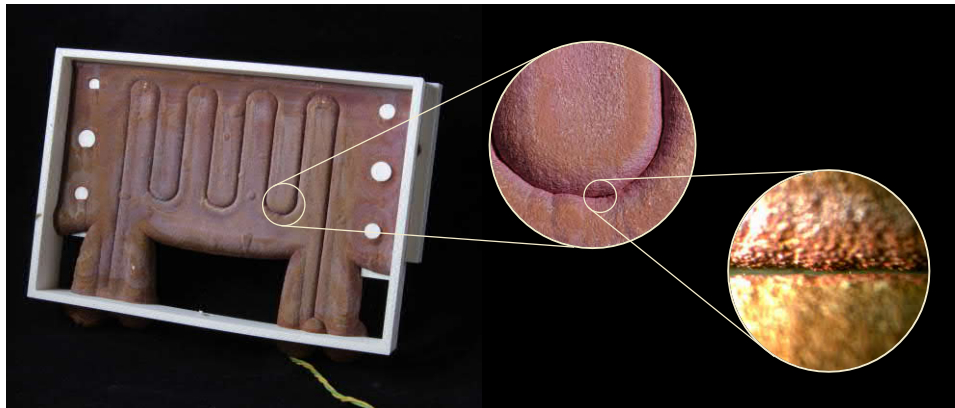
Galvanisierter Wärmetauscher ohne Aktivierung
